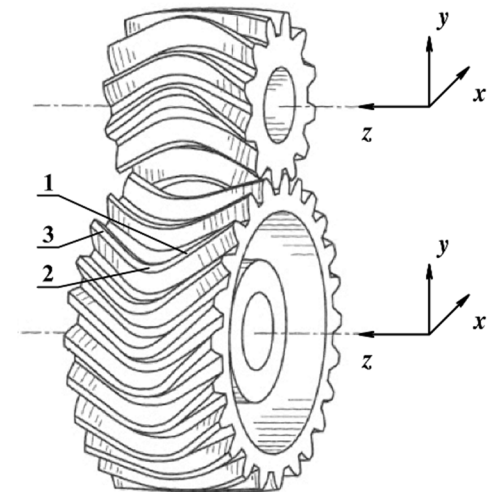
Цилиндрическая эвольвентная передача с арочно-винтовыми зубьями: 1,3 – косозубые участки; 2 – арочный участок зуба
